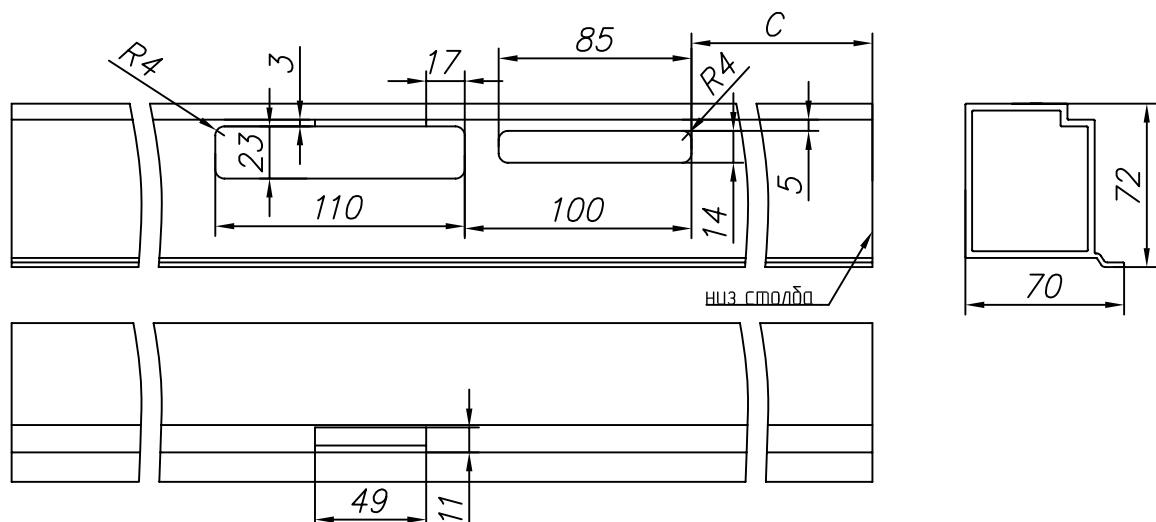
Изготовление столба притвора с пазом для автоматической защелки для калитки с левым открыванием (защелка L12HZ)
